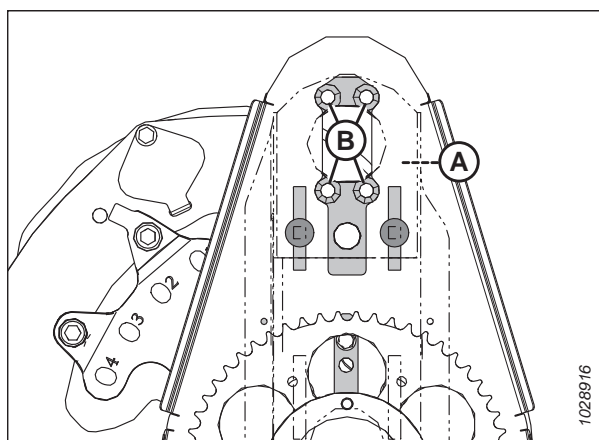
Fori di montaggio del motore di trasmissione dell'aspo
